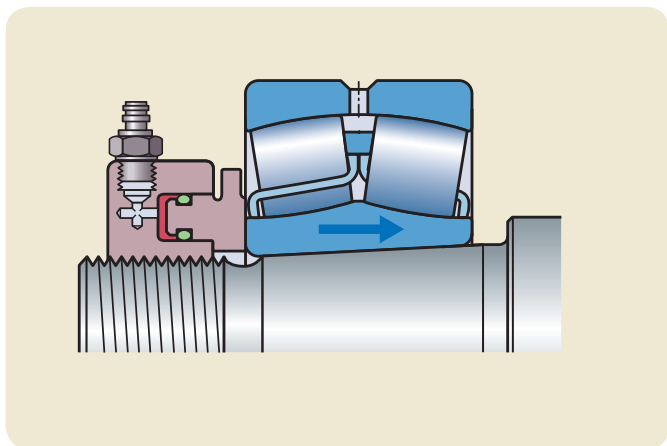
Rodamiento montado sobre un manguito de fijación y empujado.
